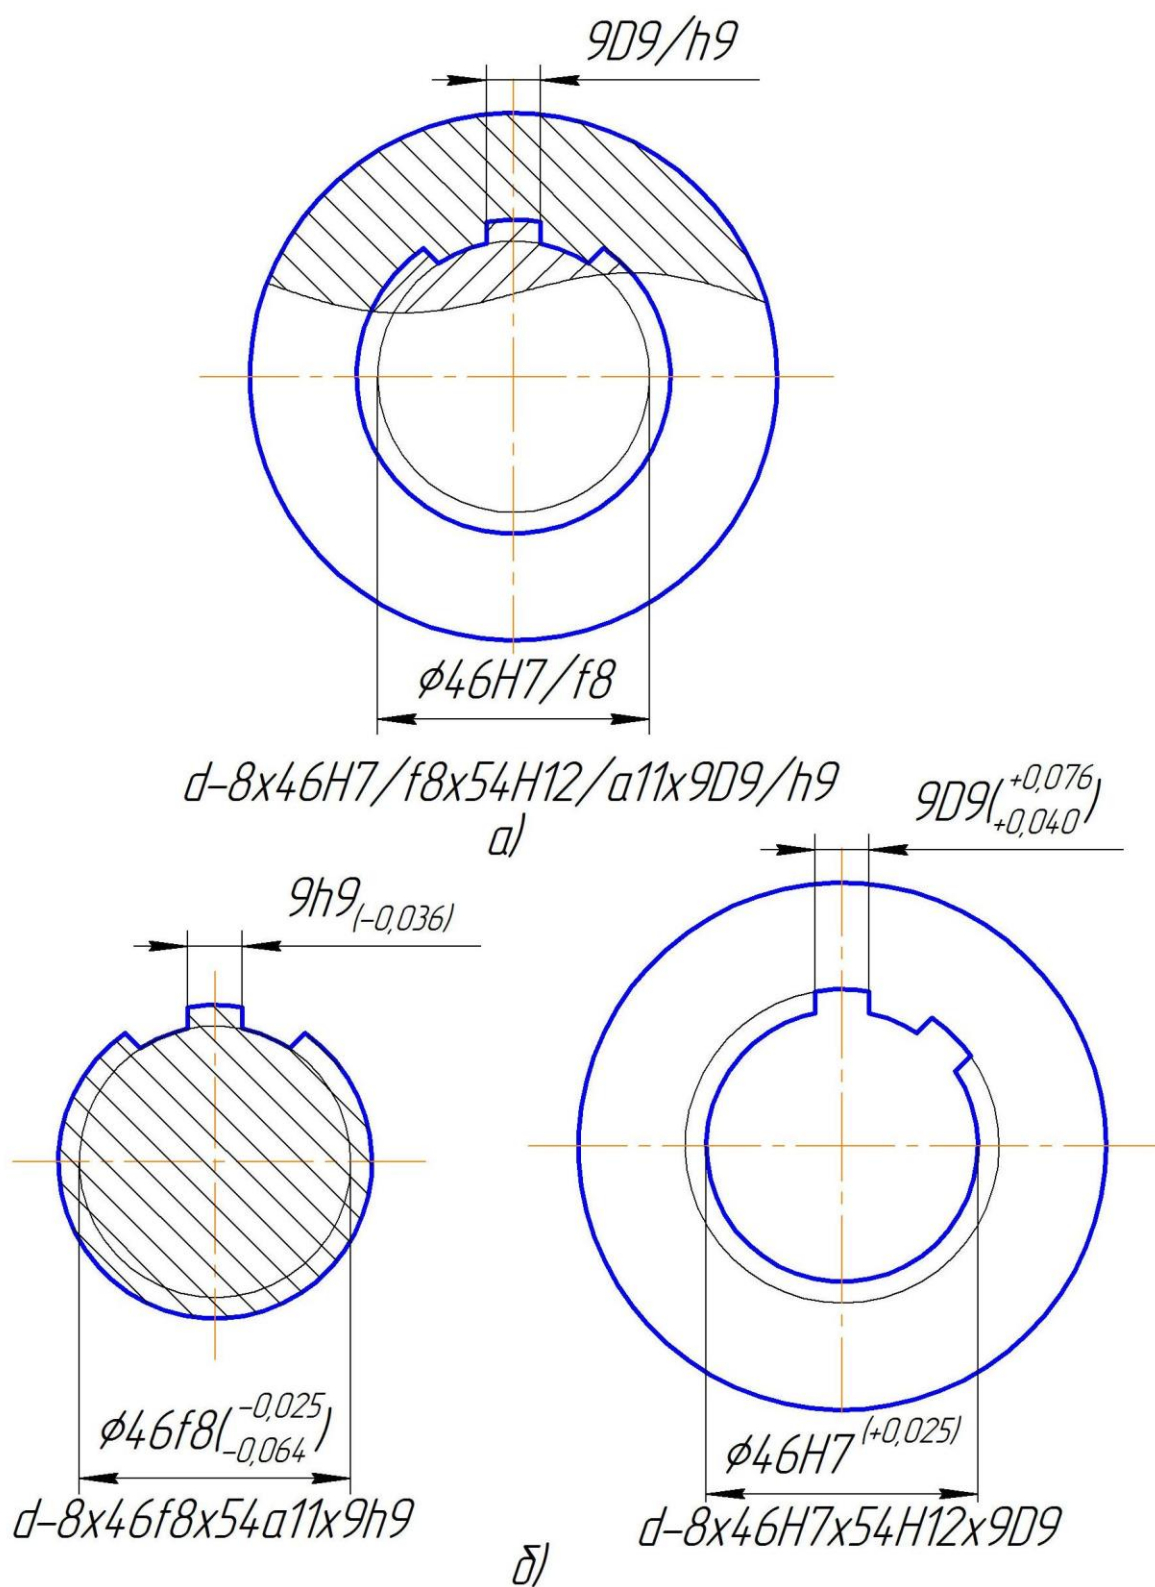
Обозначение полей допусков и посадок шлицевого соединения а) на сборочном; б) на рабочих чертежах
